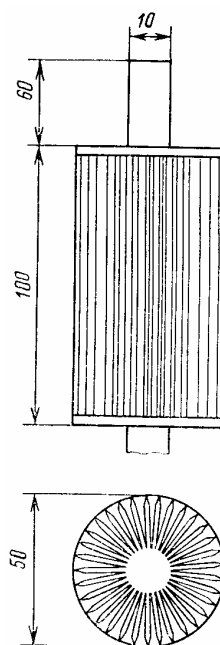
Малофазный визирный цилиндр конструкции Шишкина
